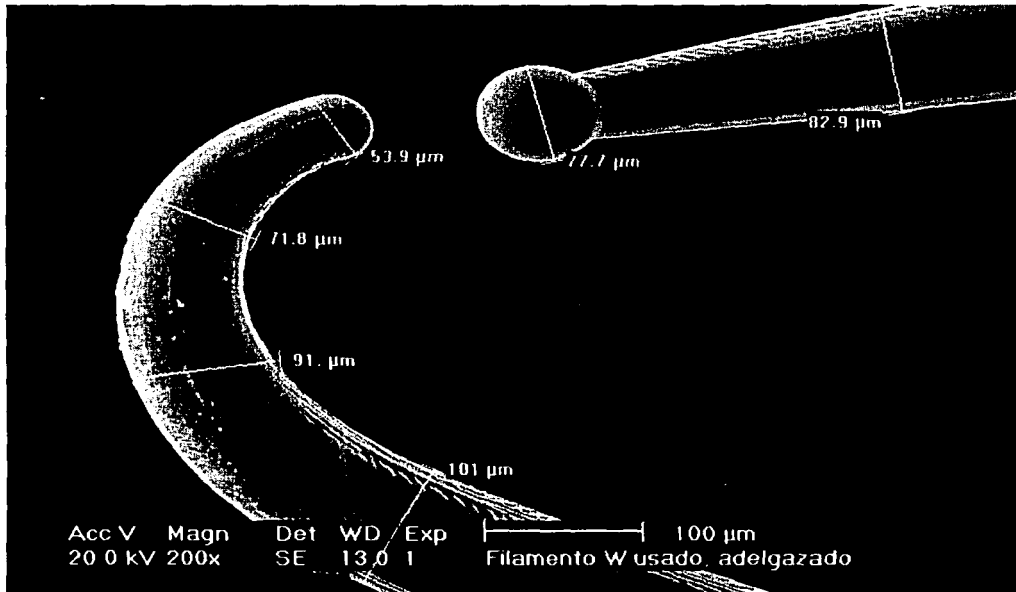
Vista de un filamento de tungsteno (falla por adelgazamiento).
